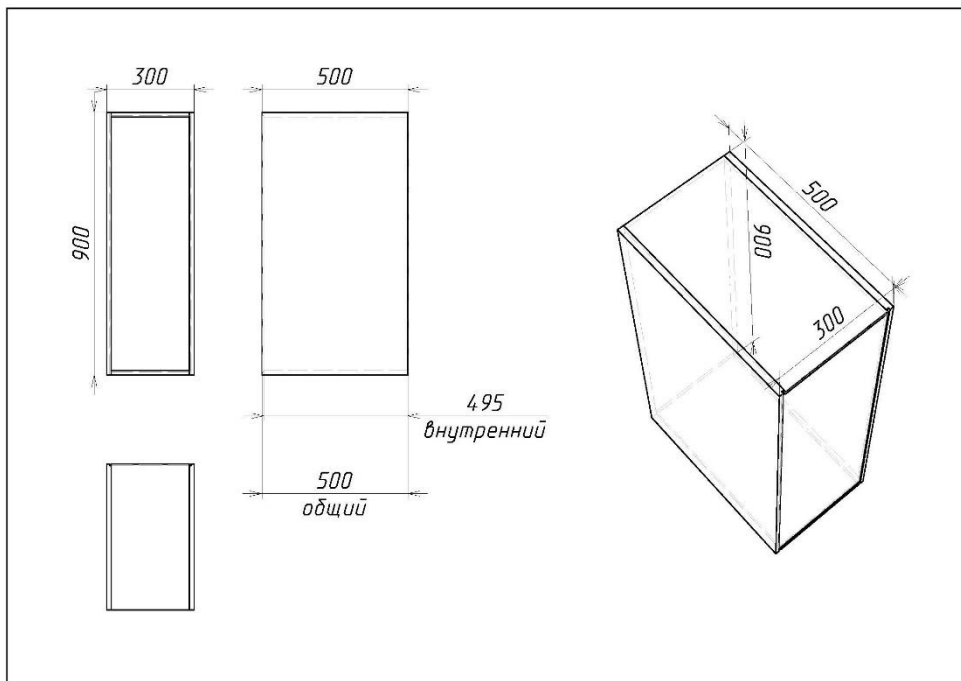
Установка задней стенки в четверть в корпус с вкладными крышкой и дном (БМ)
